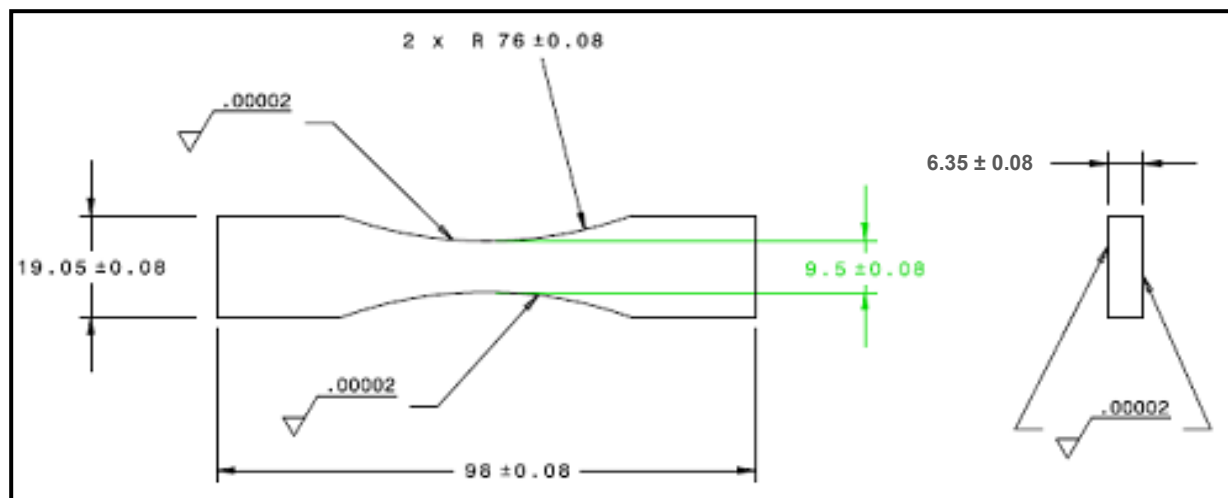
Éprouvette de fatigue sur bord lisse. Les dimensions sont en millimètres
